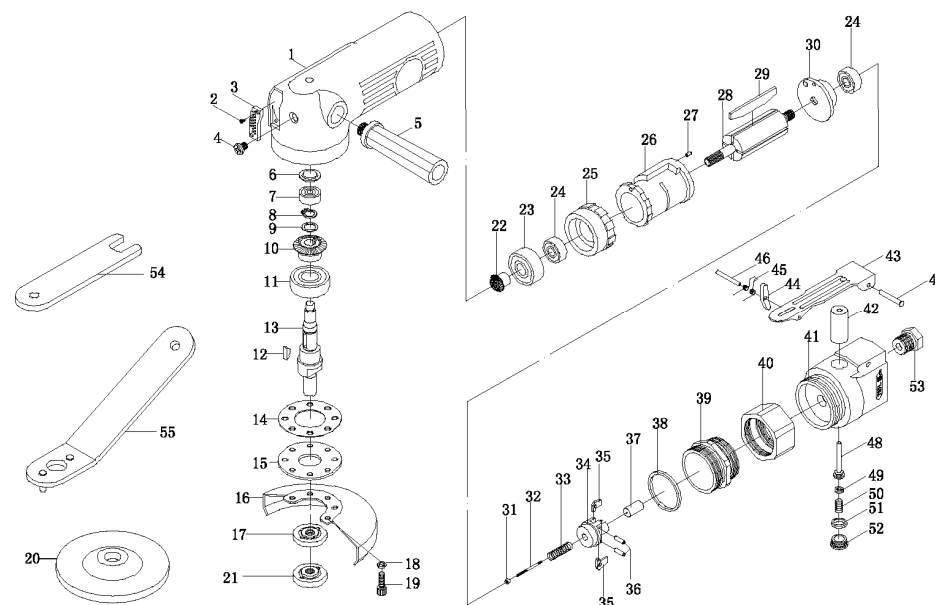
Схема устройства и сборки шлифовальной угловой пневматической MFG 125/001-1
